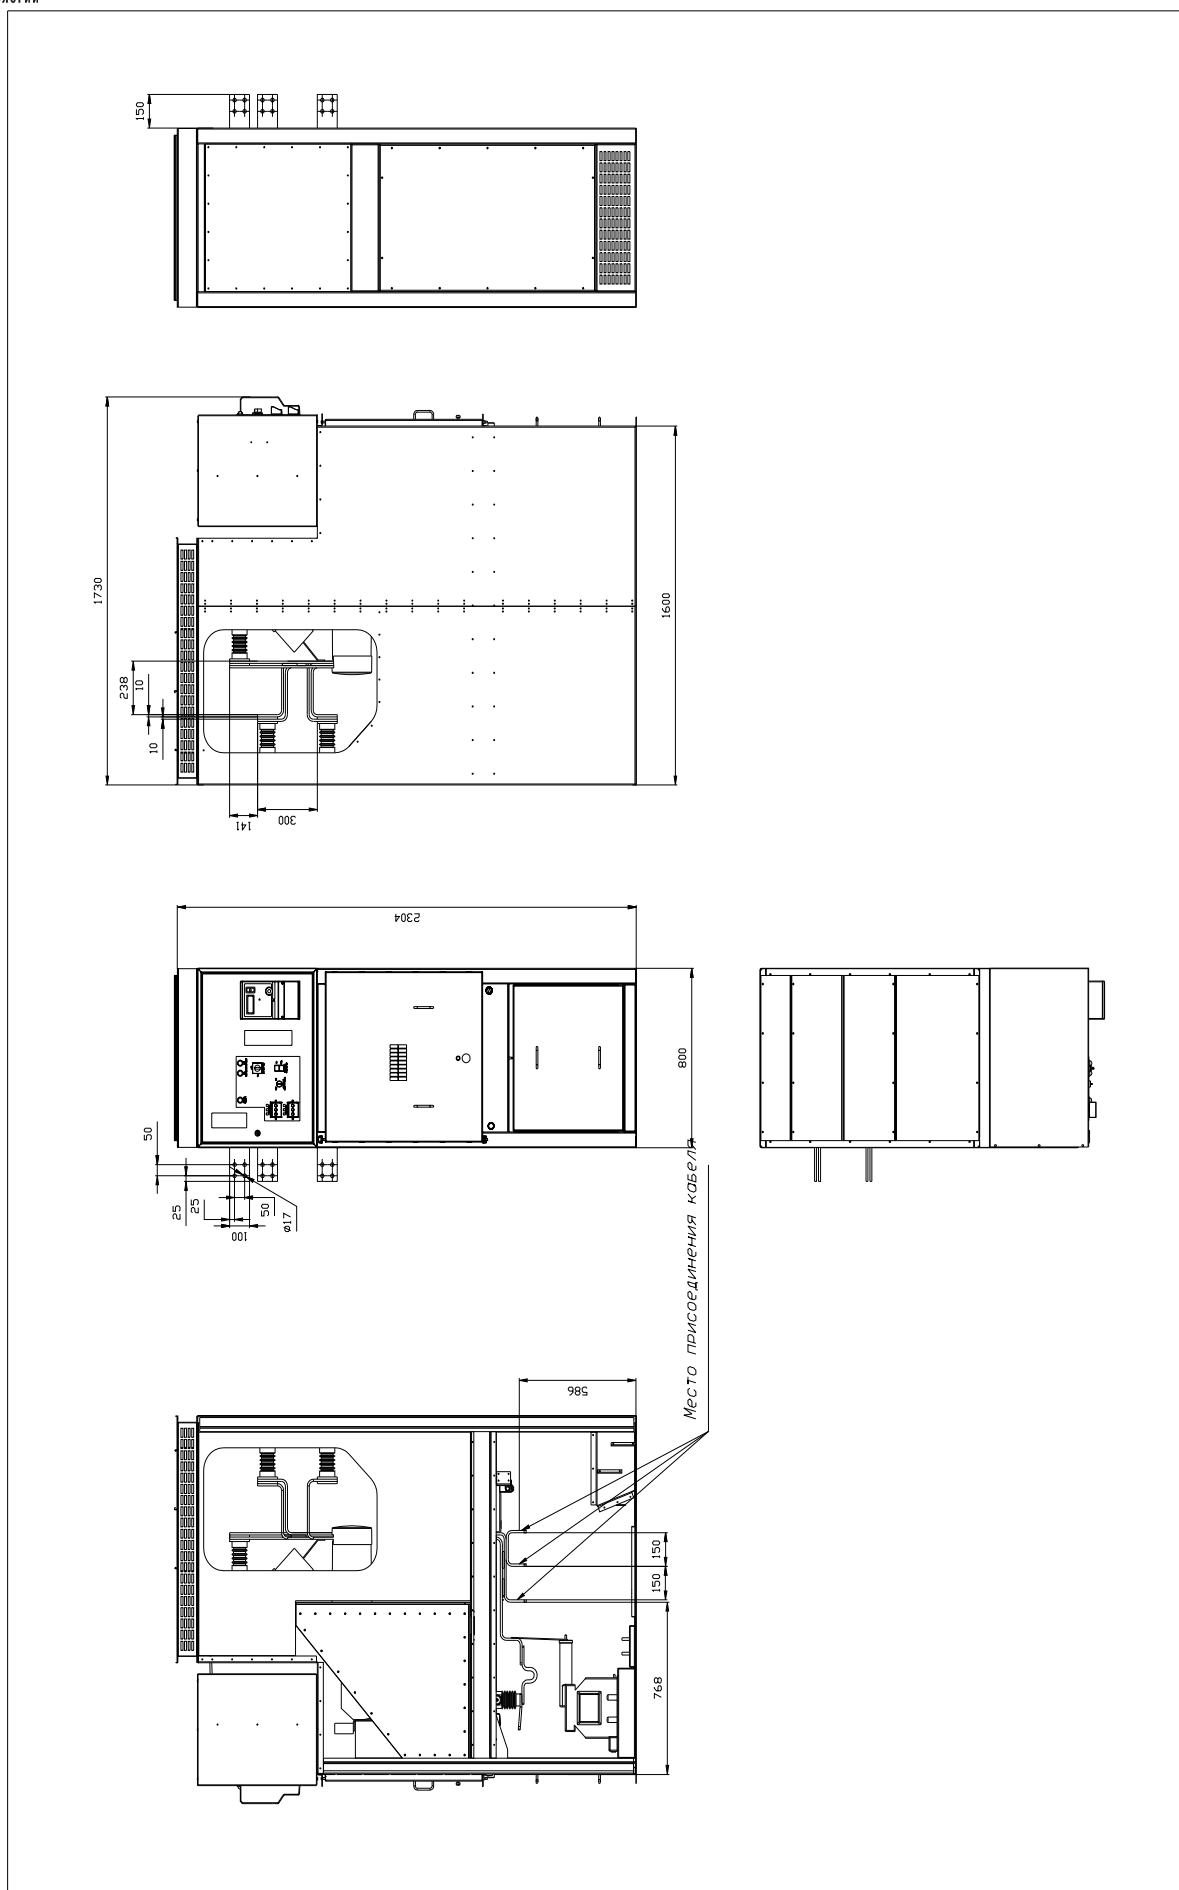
Общий вид и габаритные размеры КРУЗ-СТ10
